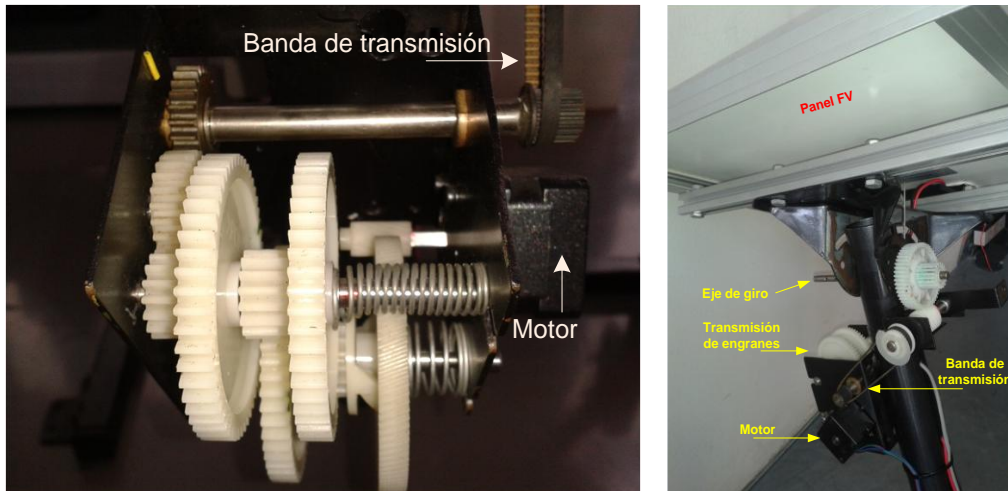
A la izquierda la transmisión de engranes, a la derecha el montaje completo
